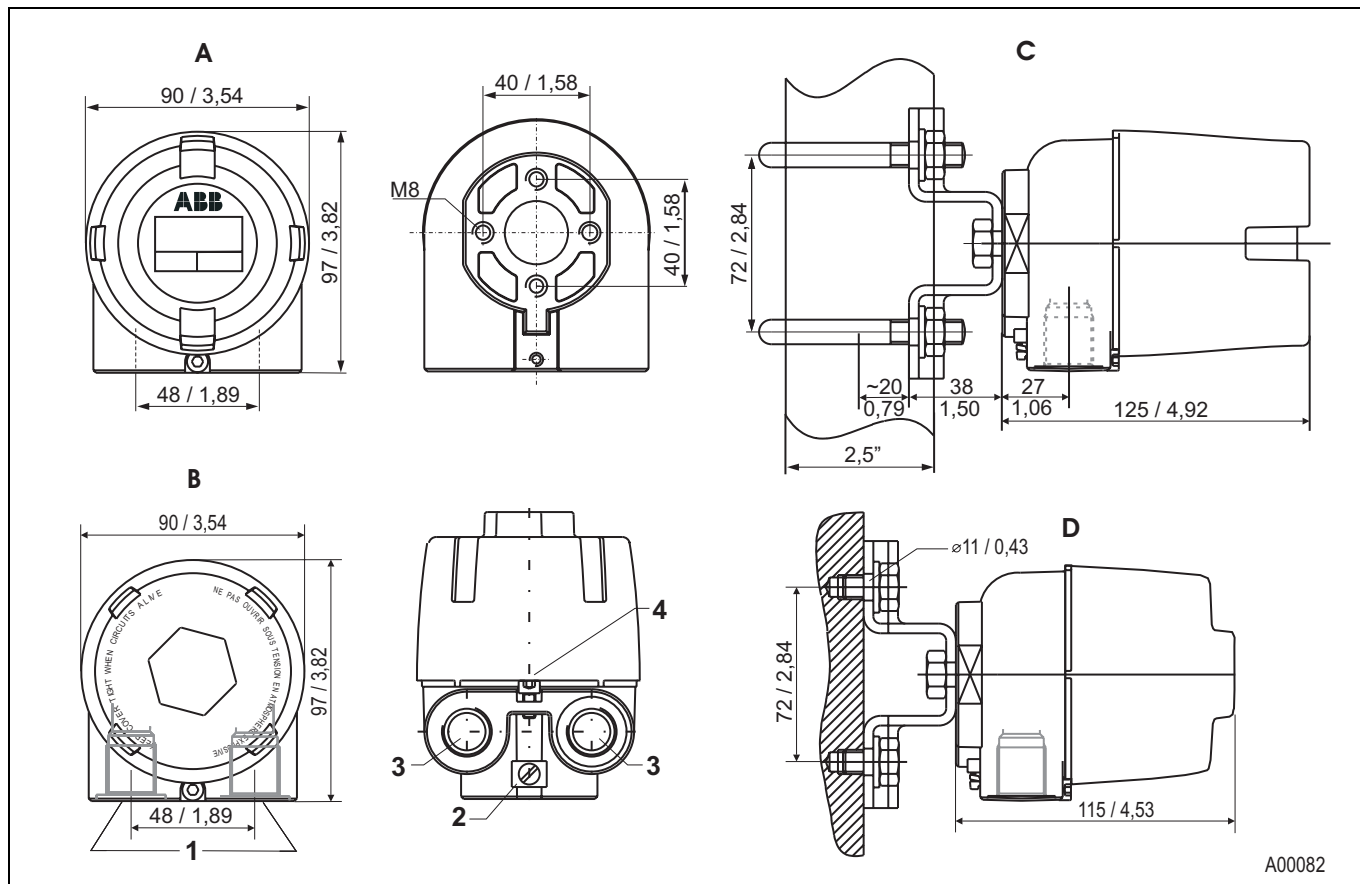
Types de boîtier et de montage avec dimensions en mm / pouces
